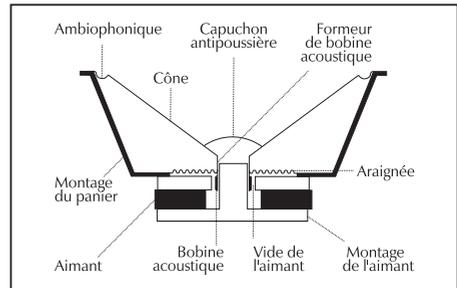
Vue en coupe d'un haut-parleur à bobine en mouvement typique. Remarquez la complexité due au grand nombre de pièces utilisées.
